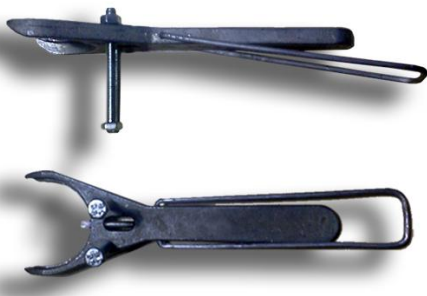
Вилка отжимная. Вид сбоку и вид сверху
